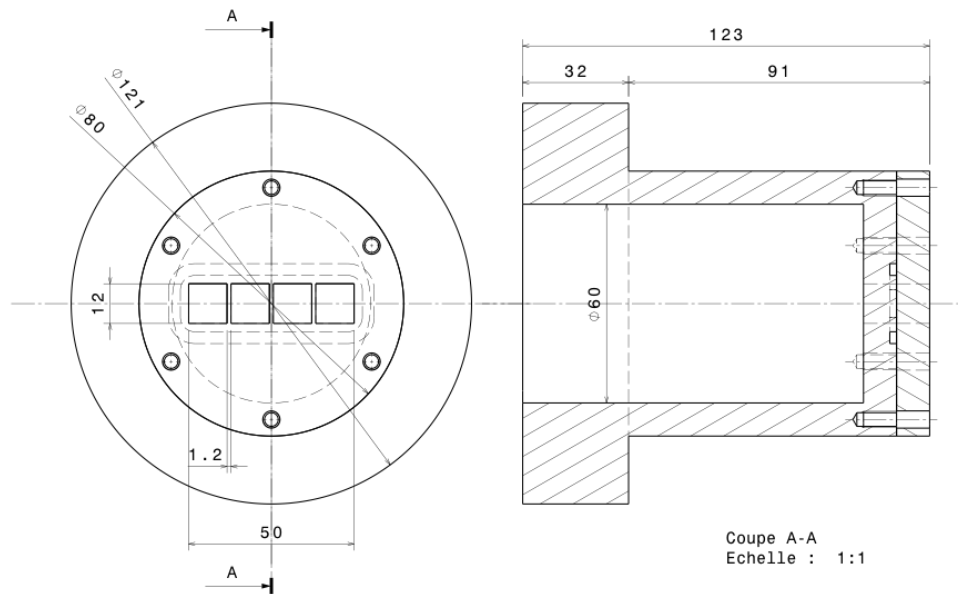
Plan de l’assemblage du manchon avec la bride maintenant la fenêtre en position.
